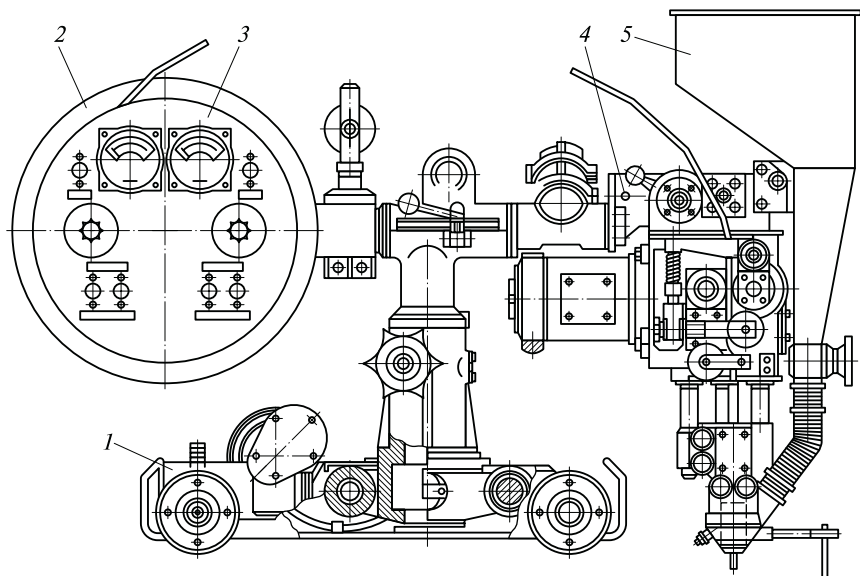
Сварочный трактор АДС-1000-2:
